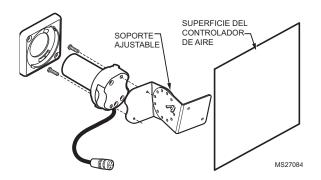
Ensamble del soporte de montaje en ángulo a la superficie interna.
